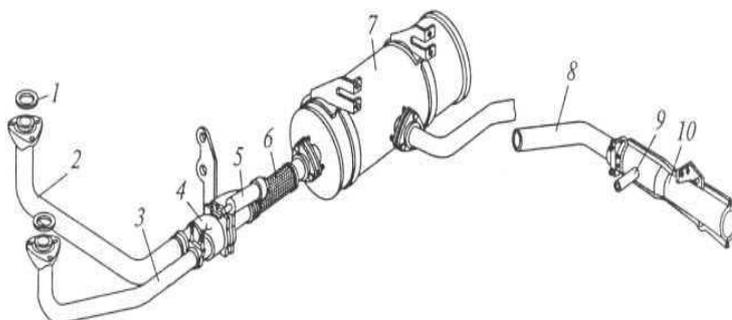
Схема системы выпуска отработавших газов дизеля: 1 - уплотнитель; 2, 3, 8 - трубы; 4 - тормоз-замедлитель; 5 - пневмо-цилиндр; 6 - рукав; 7 - глушитель; 9 - патрубок; 10 - эжектор
